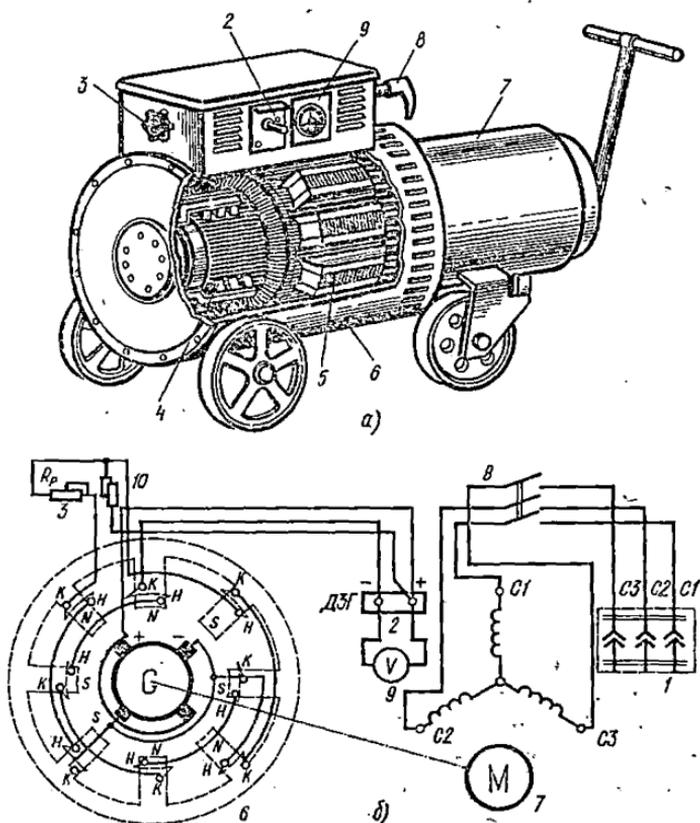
Сварочный преобразователь ПСГ-500-ІУЗ:
